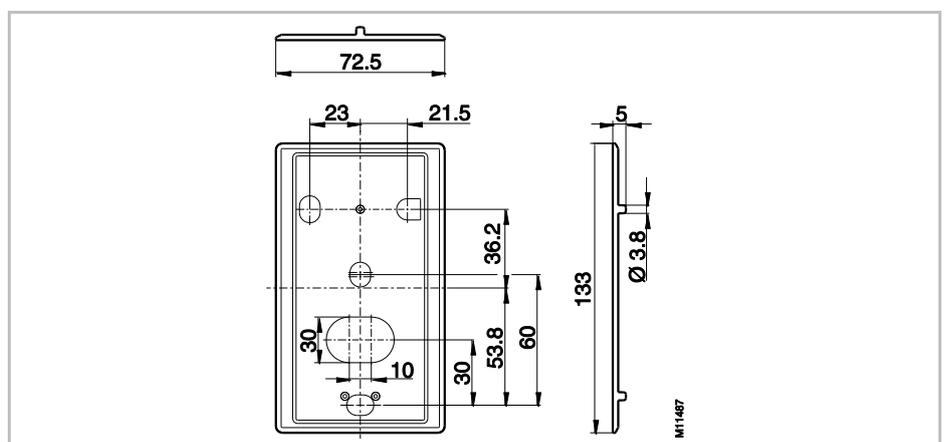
Abmessung Abdeckplatte (alle Maße in mm)
